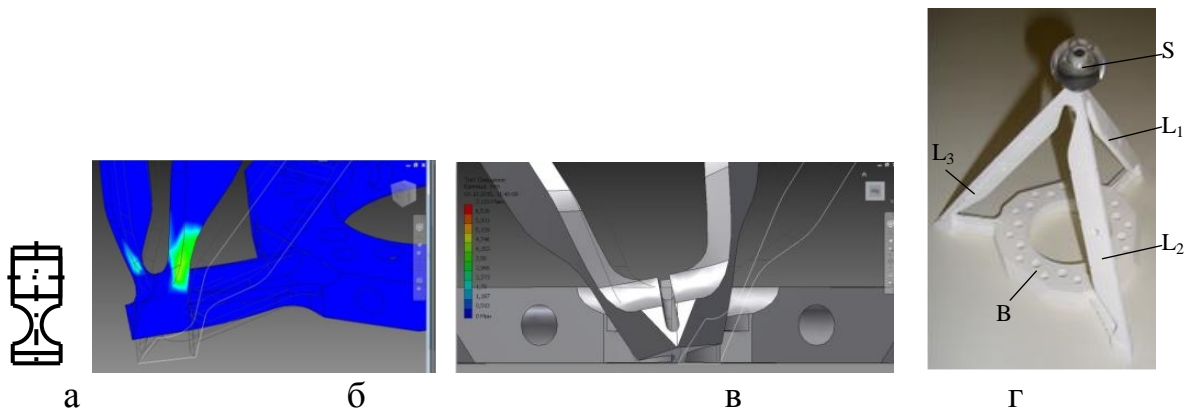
Пружні шарніри з круговими фасонними виборками: а – двохкоординатний пружний шарнір; б – вигляд спереду подвійного пружного шарніра; в – розрахунок напружено-деформованого стану шарніра (вигляд збоку); г – застосування пружних шарнірів у приводі мікропереміщень тетрадрального виду із плоскими пружинами
